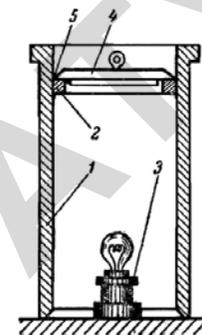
Приспособление для проверки прилегания кольца к зеркалу цилиндра: 1 – гильза цилиндра; 2 – поршневое кольцо; 3 – лампочка; 4 – диск; 5 – щуп
